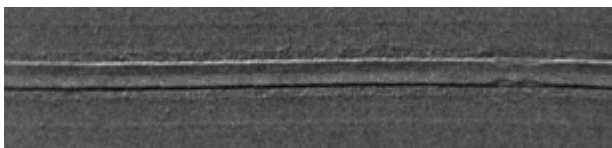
Probe 10, DC04+ZE; Spalt 0,2 mm
